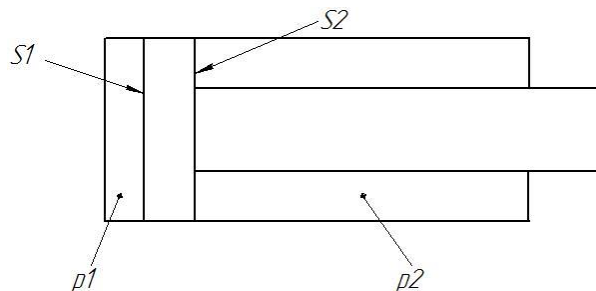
Розрахункова схема гідравлічного циліндра
